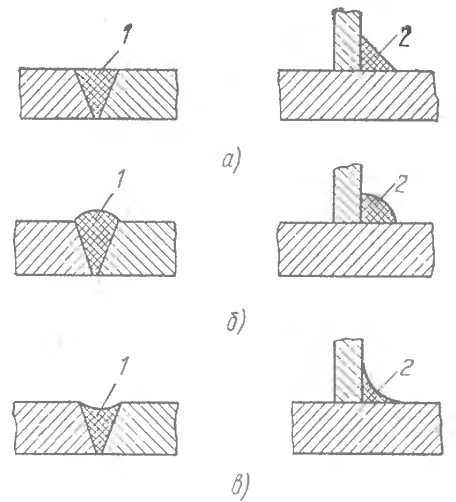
Классификация сварных швов по форме внешнего контура сечения шва:
